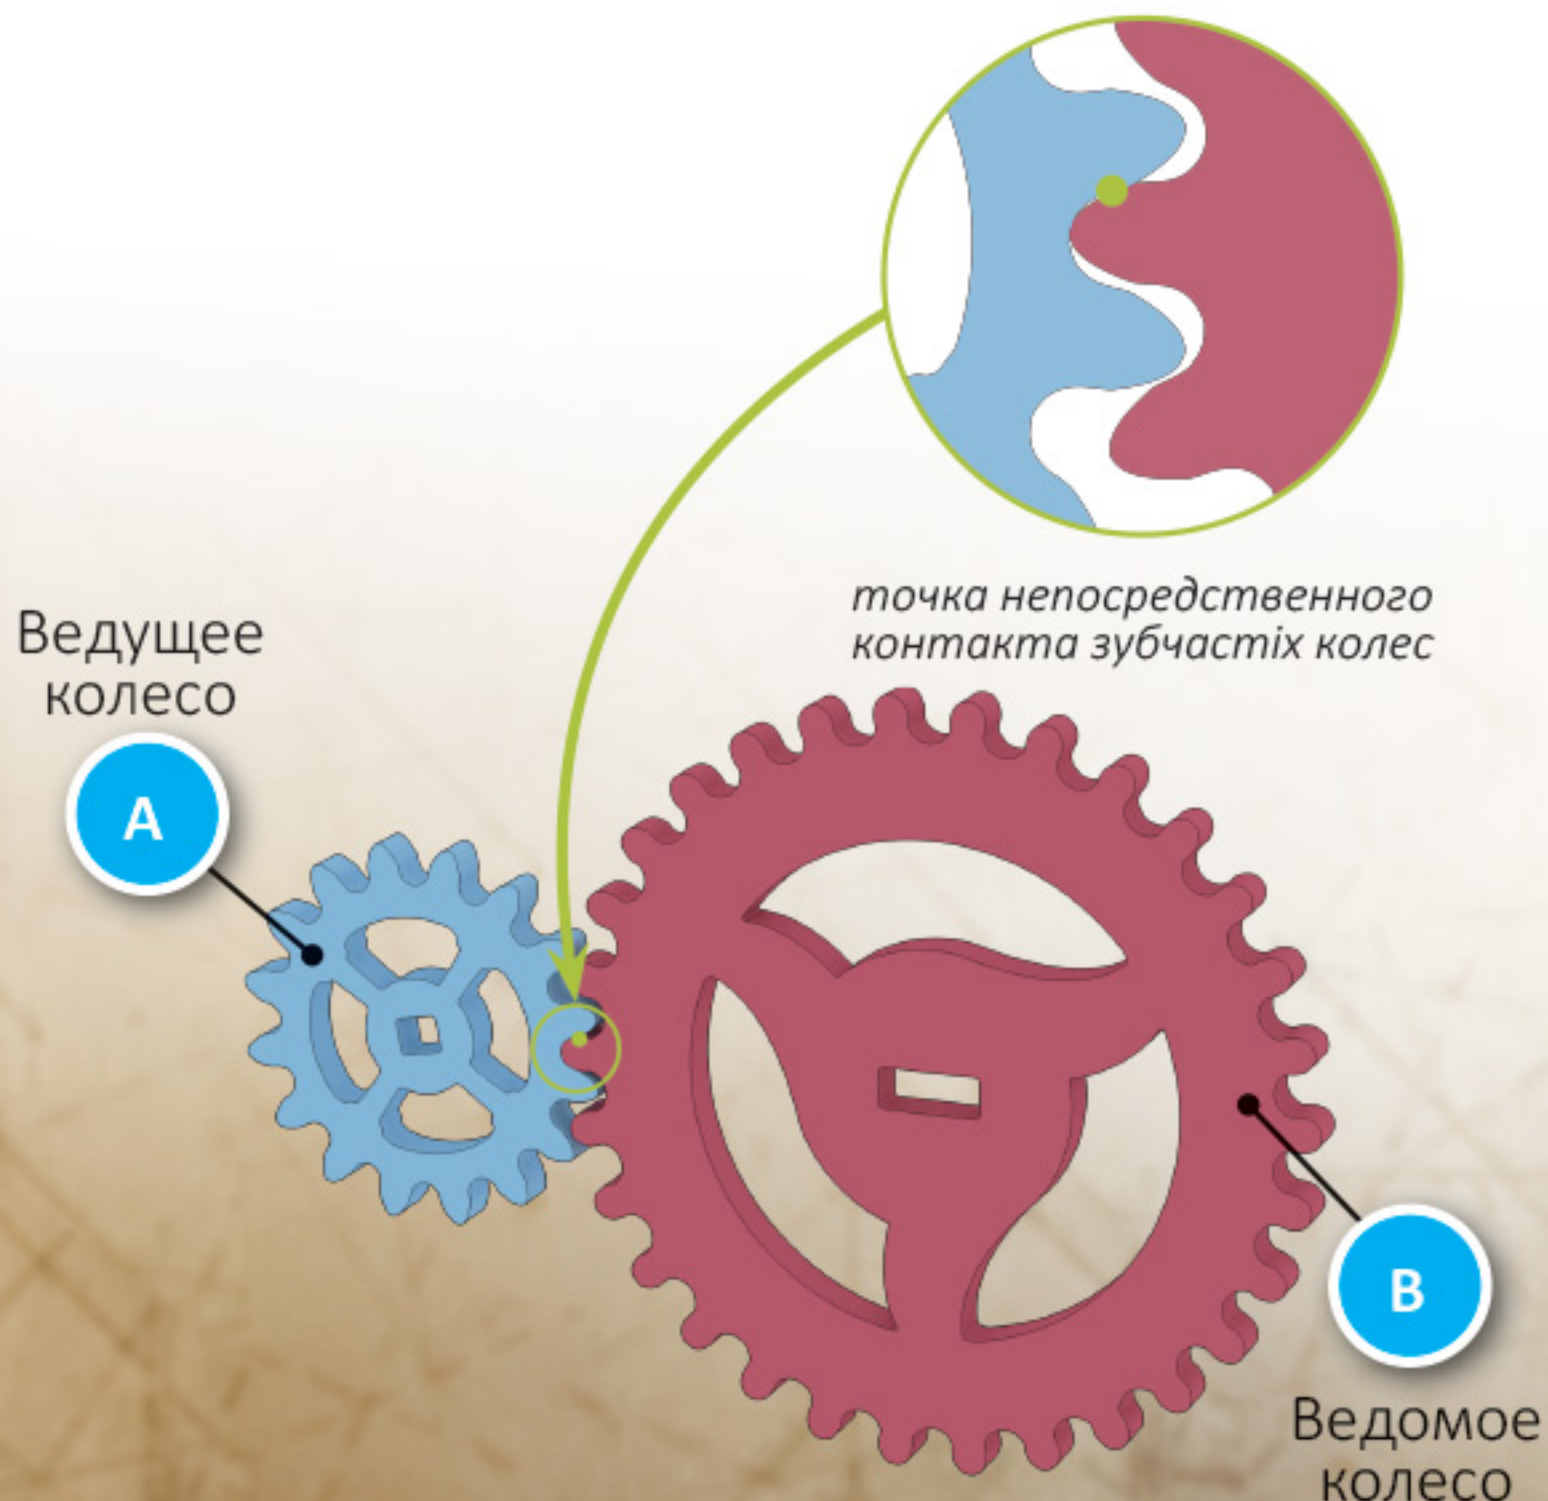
Зубчатая передача (пример зацепления зубчатых колес)
